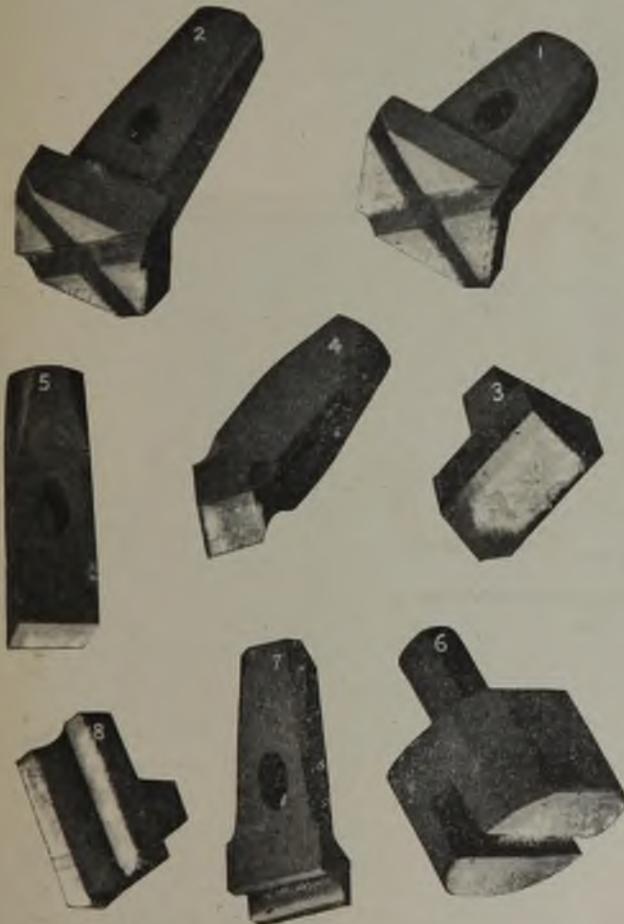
Gesenke und Aufhauwerkzeuge für das Ausschmieden der Bohrmeißel. Pratt Machinery Co., Chicago.
